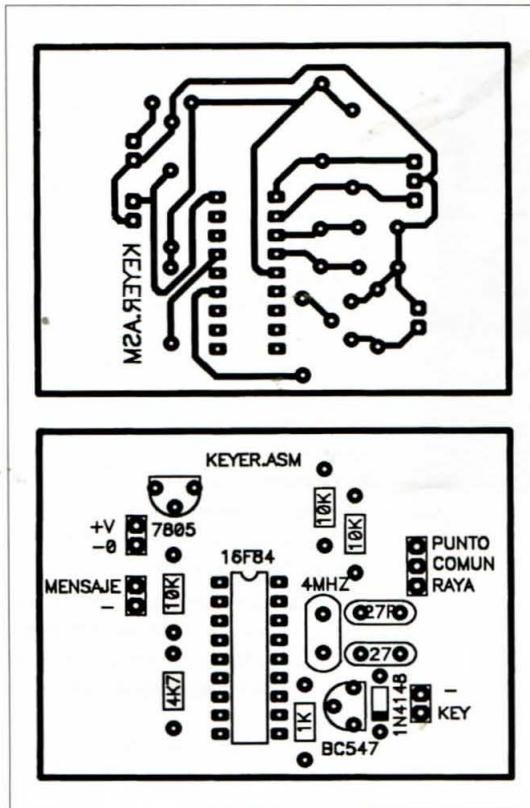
Cara de pistas y cara de componentes de la plantilla del circuito impreso para el manipulador con memoria.
